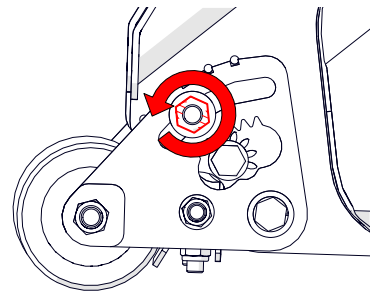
E - Desserrer l'écrou de serrage supérieur du quadrant du rouleau.
